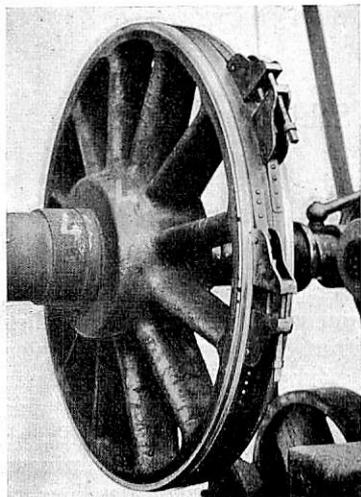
Einpressen des Aluminiumbleches mit Hilfe zweier Stahlbänder.
